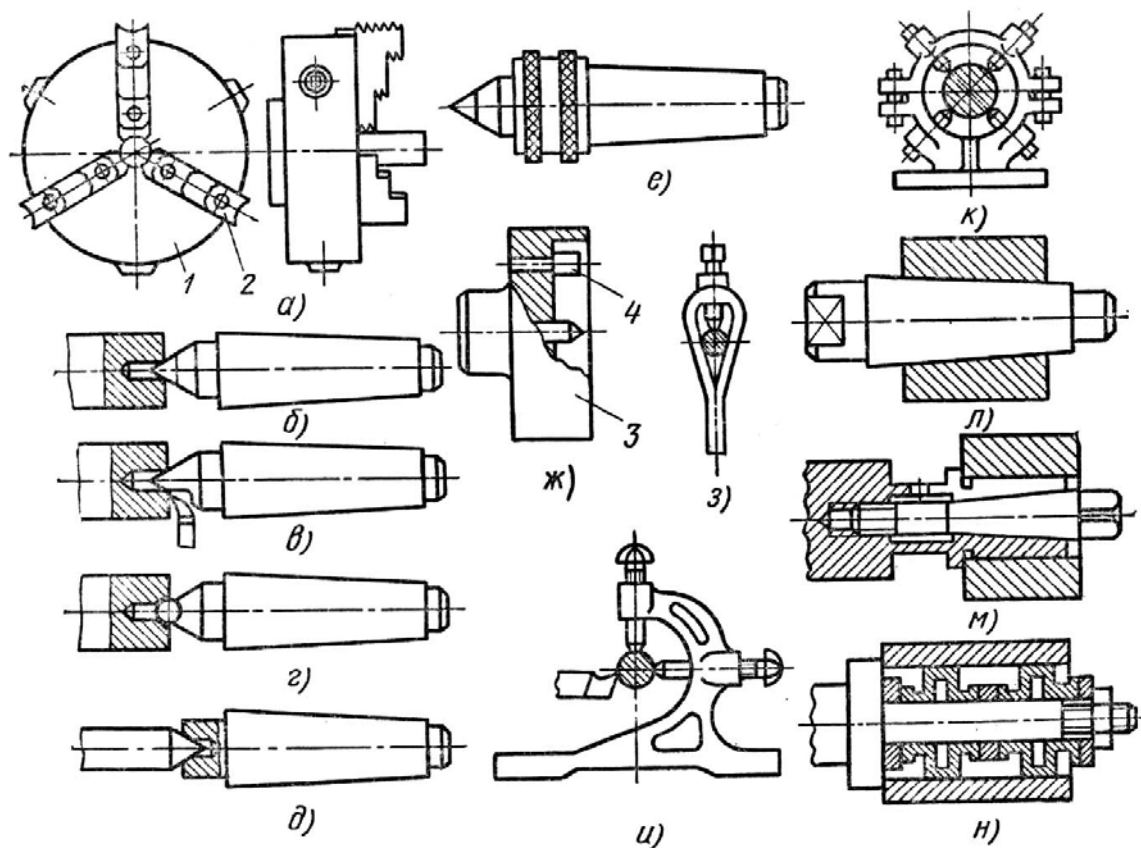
Приспособления для закрепления заготовок на токарных станках: *а* – патрон (самоцентрирующий или несамосцентрирующий); *б* – упорный центр; *в* – срезанный центр; *з* – центр со сферической рабочей частью; *д, е* – вращающиеся центры; *ж* – поводковый патрон; *з* – хомутик; *и, к* – люнеты; *л* – коническая оправка; *м* – цанговая оправка; *н* – упругая оправка
